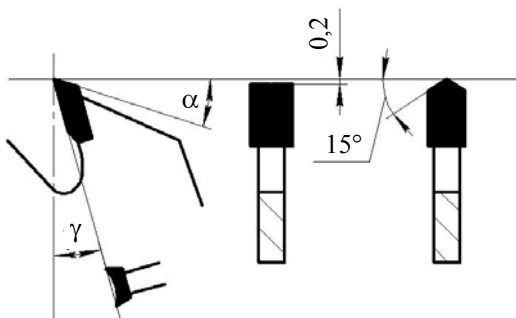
Елочно-плоский с вогнутой передней гранью профиль зубьев дисковых пил с пластинами твердого сплава для распиловки ламинированных ДСтП
